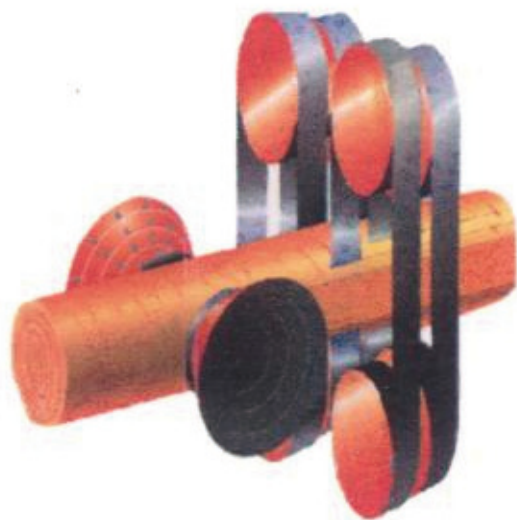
Компоновка фрезернопильного агрегата (ФЛПА).
